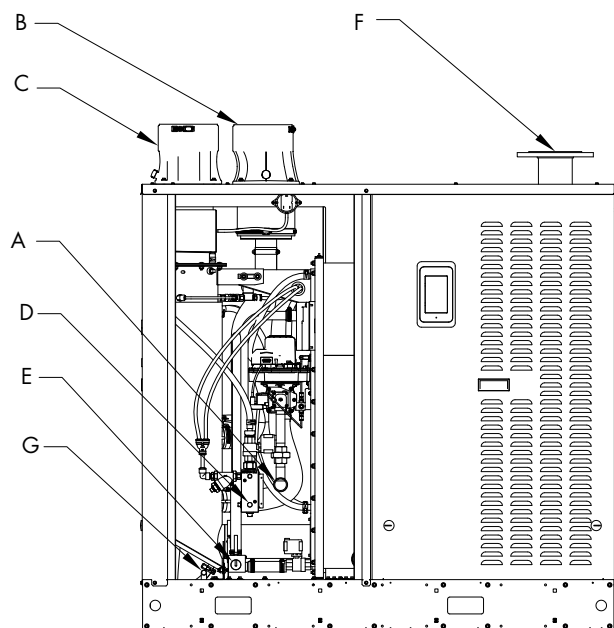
DÉTAILS DU RACCORDEMENT GTS LX 200 - 300
